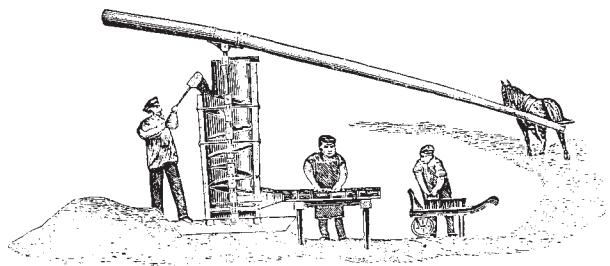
Stehender Tonschneider mit Tierbetrieb über Zugbaum
